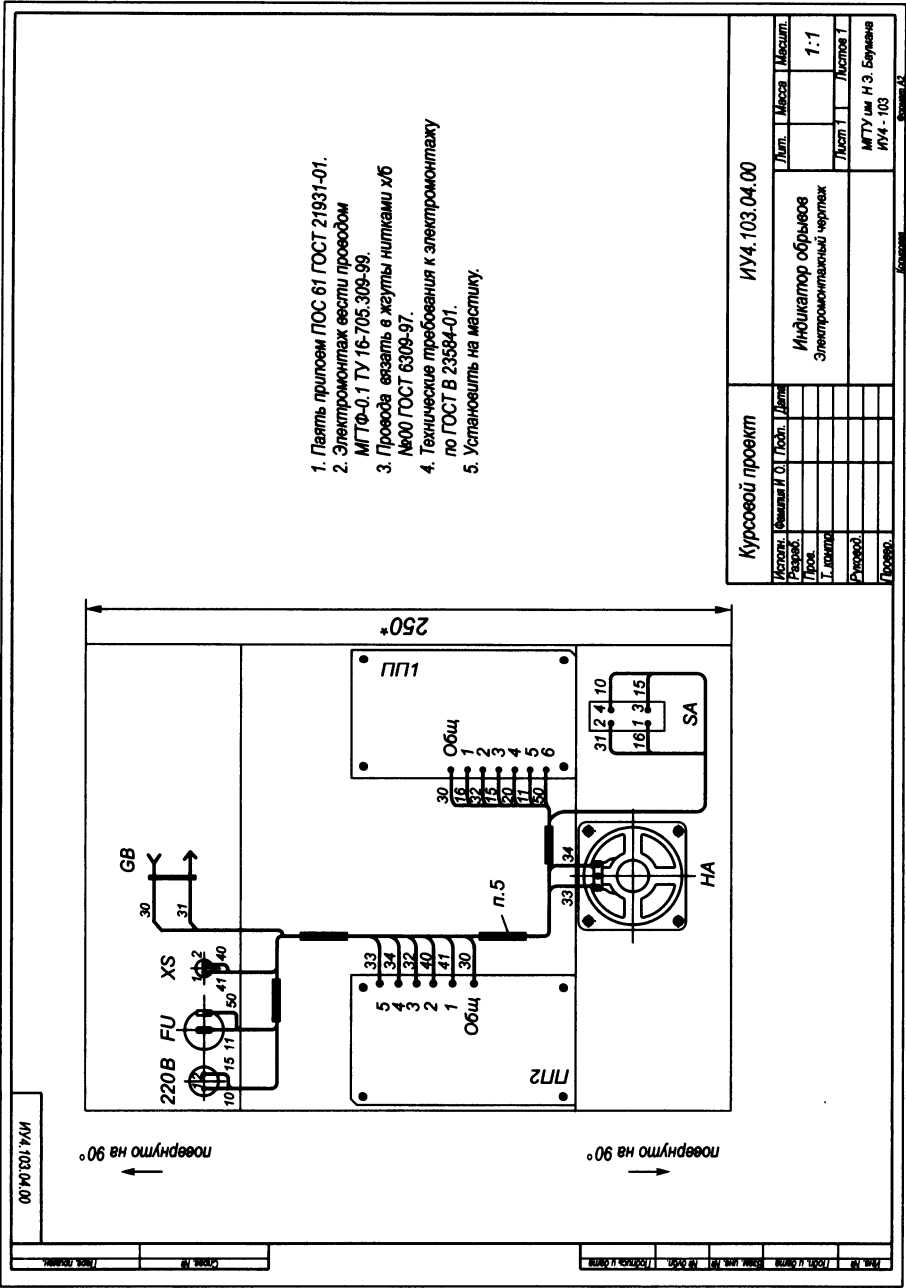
Индикатор обрывов. Электромонтажный чертеж
